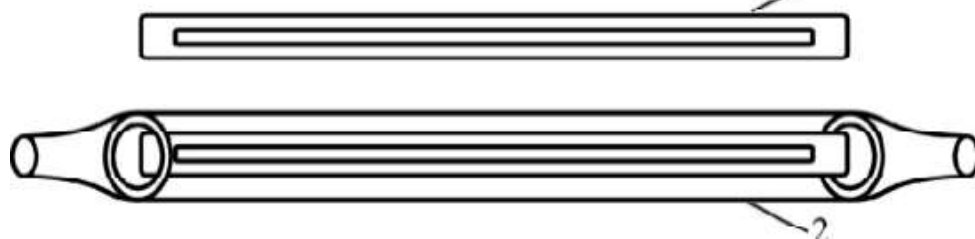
«Жакетирование» заготовки: 1 – исходная заготовка, 2 – заготовка в дополнительной кварцевой трубке
